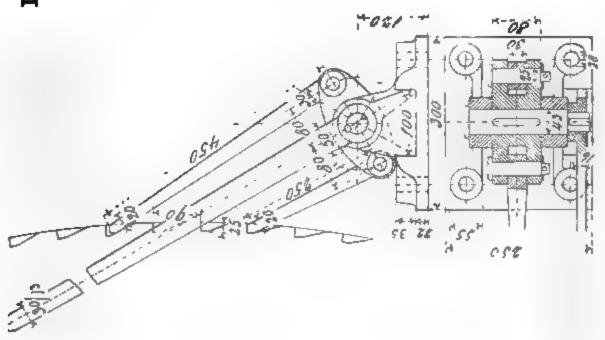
775. Für kleinere u. mittlere Maschinen.
